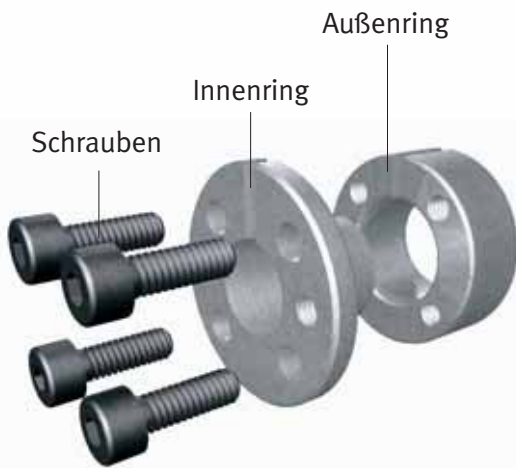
Befestigung einer Zahnriemenscheibe mit MAV 2061
